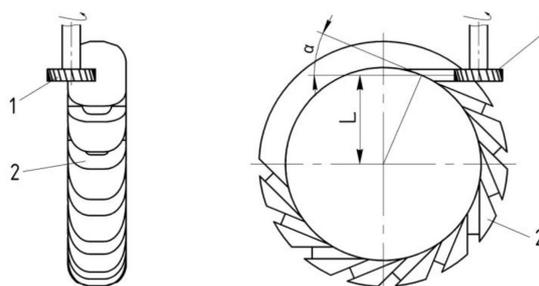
Схема фрезерования МЛК дисковой фрезой: 1 – дисковая фреза; 2 – заготовка
